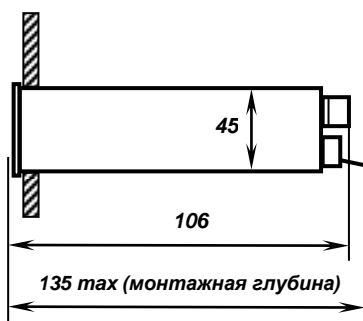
Внешний вид индикатора ИТМ-100
